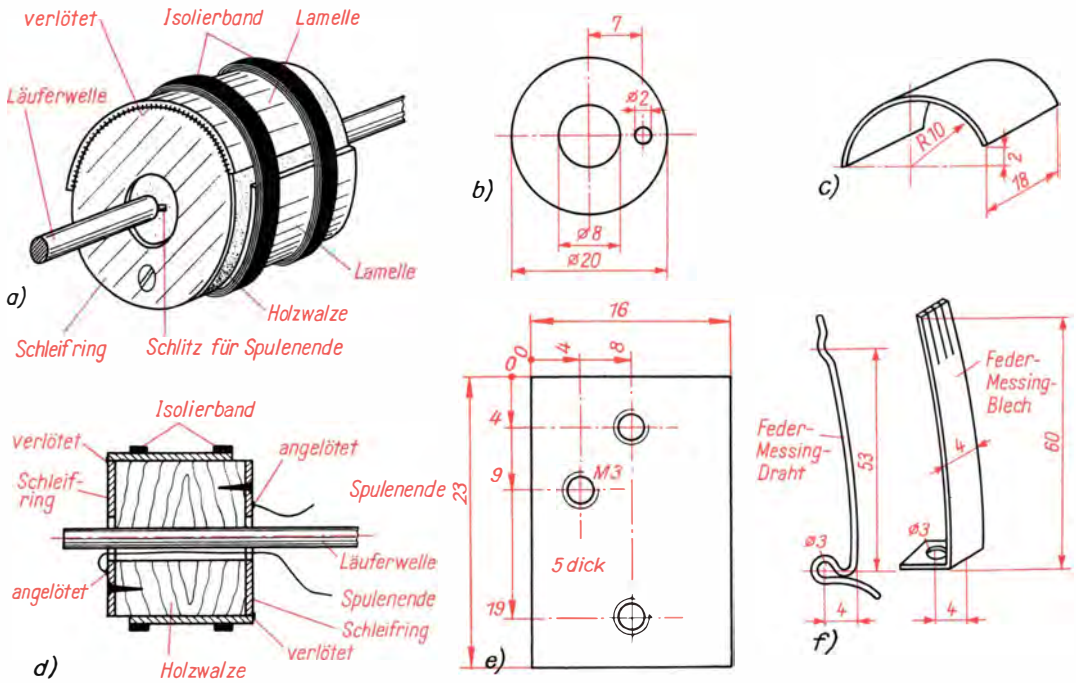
Der Kollektor und das Bürstenbrettchen: a) Kollektor mit Schleifring-Lamellenträger, b) Schleifring, c) Lamelle, d) Schnitt durch den fertigen Kollektor, e) Bürstenbrettchen, f) mögliche Bürstenkonstruktionen
